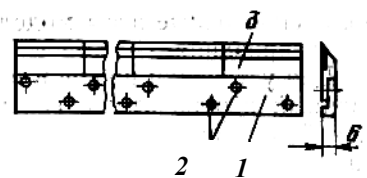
Сборный нож с секциями, оснащенными пластинами из твердого сплава:
